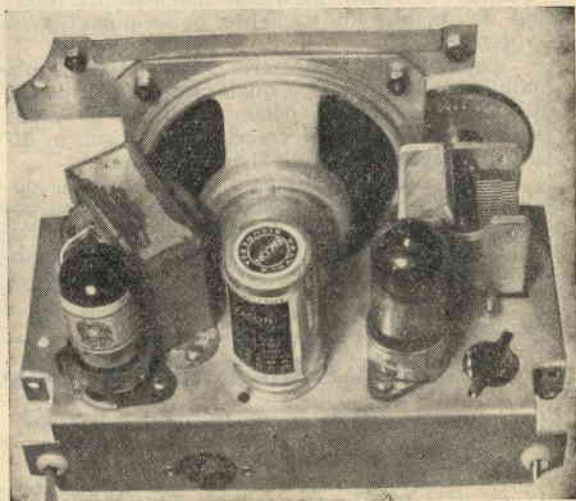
Foto dall'alto della parte superiore dello chassis con componenti montati.
